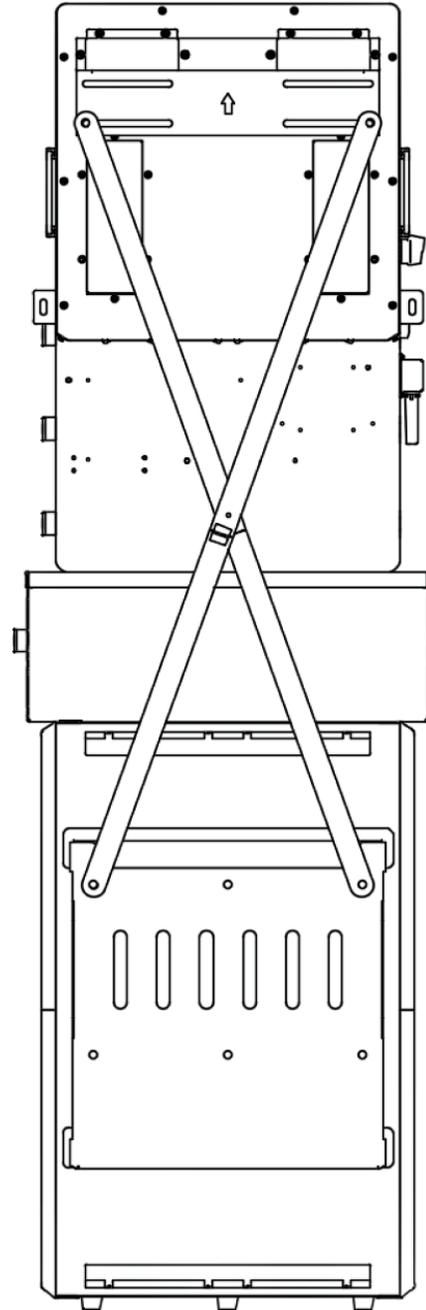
WallMount Instalación con Caja de Conducto y 18kPV Pasos 5 y 6
